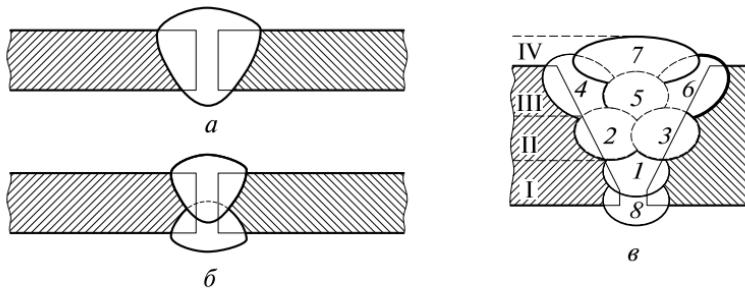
Одно- (а) и двусторонний (б) однопроходные однослойные швы и многопроходный многослойный сварной шов (в):
